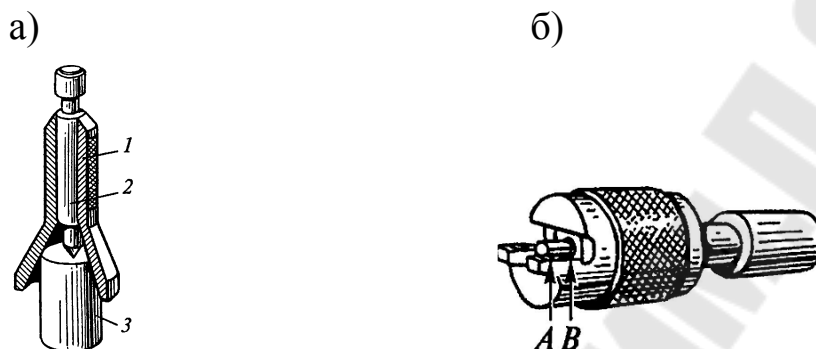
Приспособление для накернивания центровых отверстий без предварительной разметки (а) и пример применения калибр-втулки для проверки наружных конусов (б)
